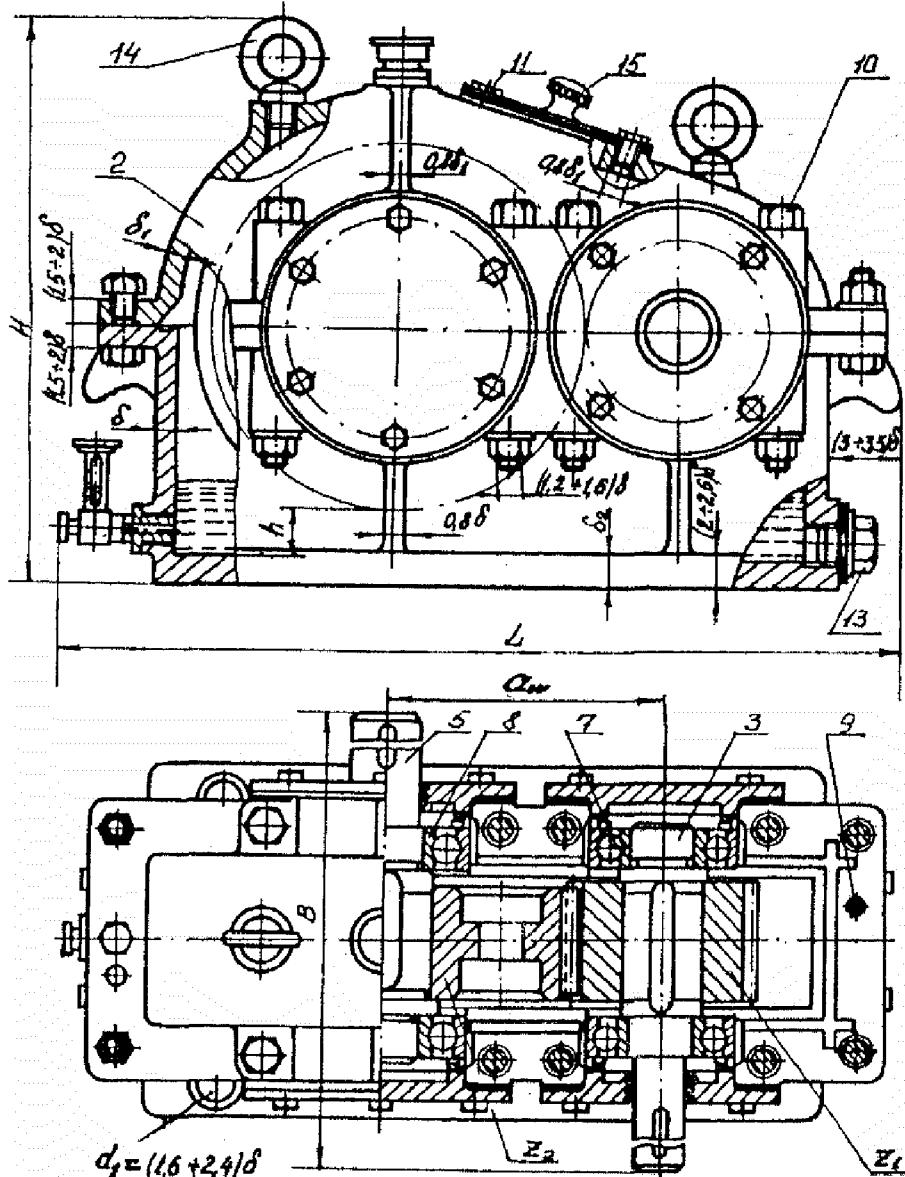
Одноступінчастий редуктор з циліндрическими колесами
